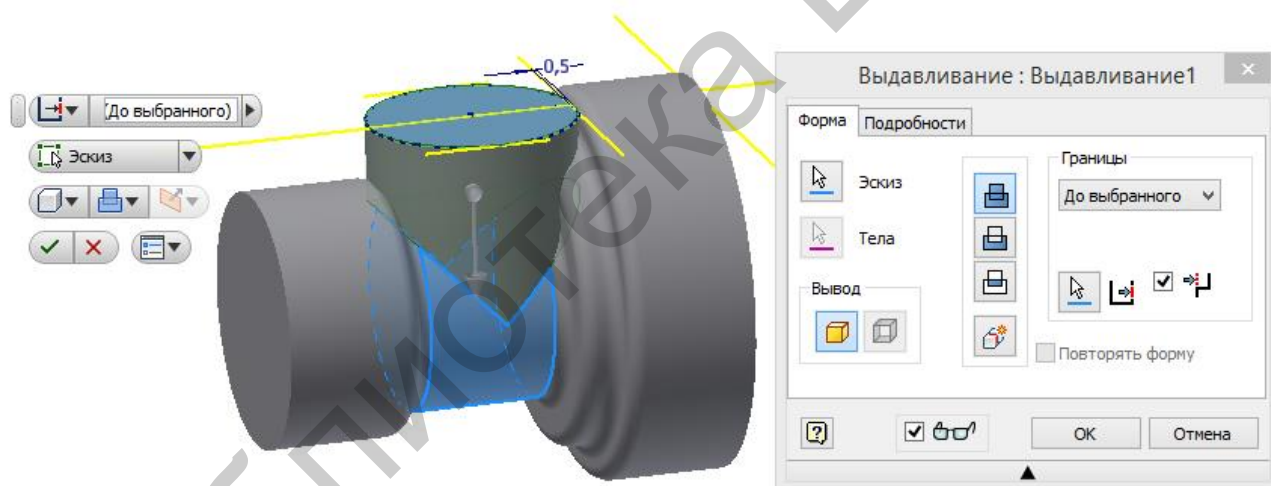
Вторая стадия формообразования заготовки корпуса
